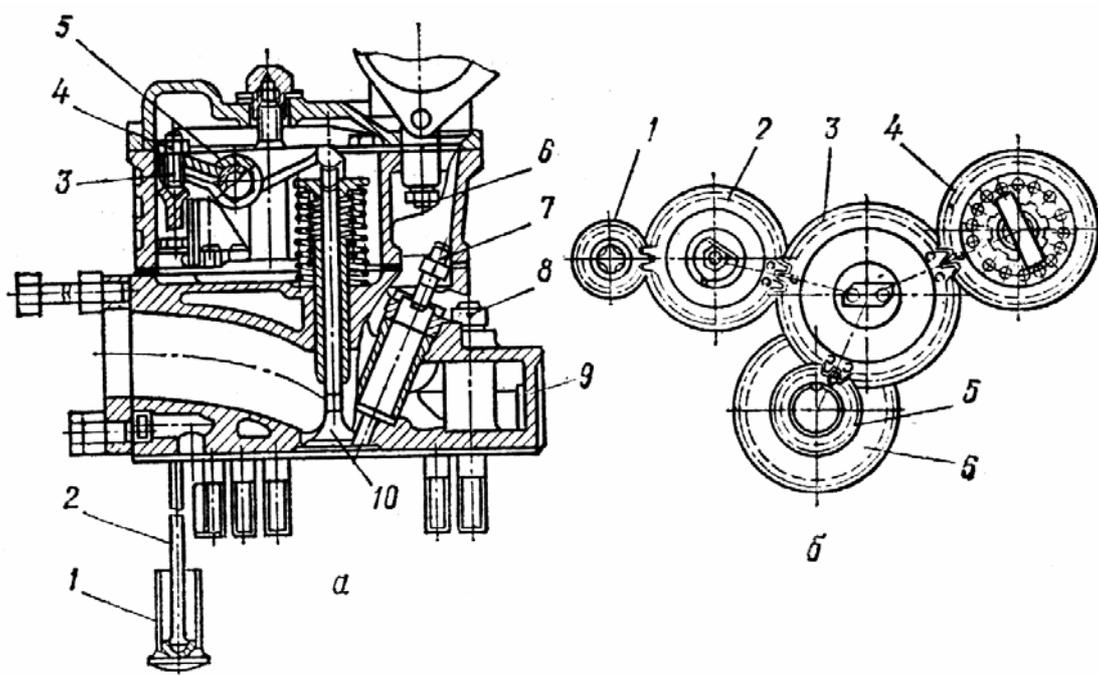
Газораспределительный механизм двигателя Д-240:
